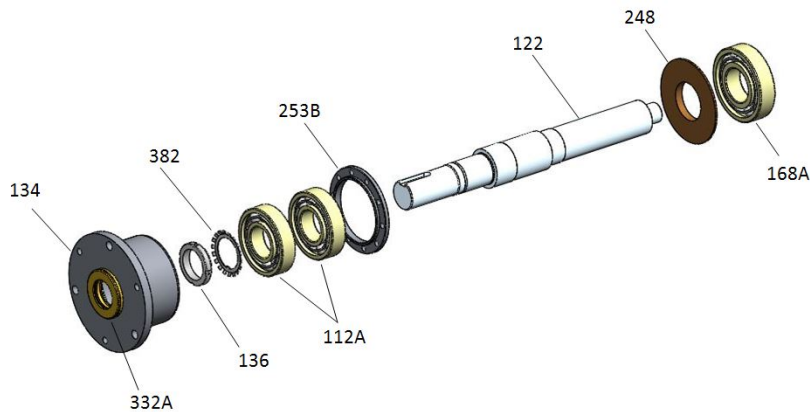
Montaje de la flecha- rodamiento doble-Grupo 3
